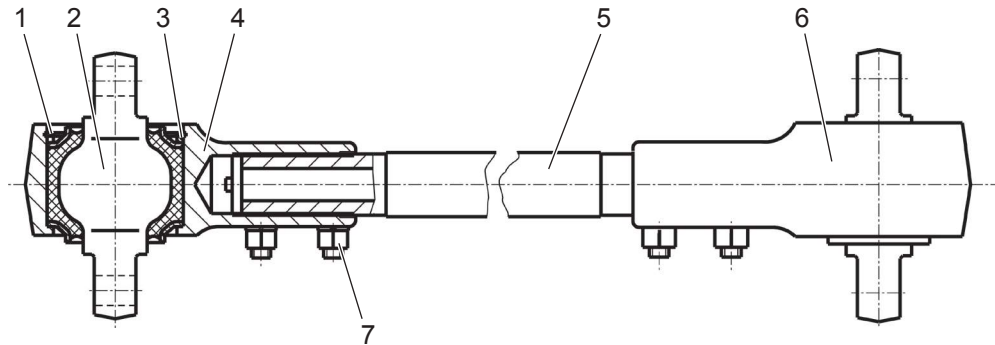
Реактивная штанга задней подвески:
